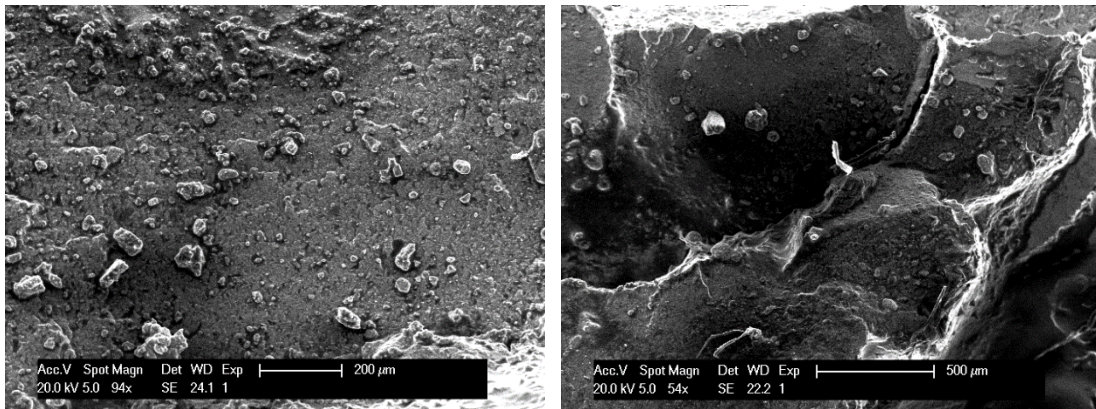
Schwingbruchfläche (li); Restgewaltbruchfläche (re)
